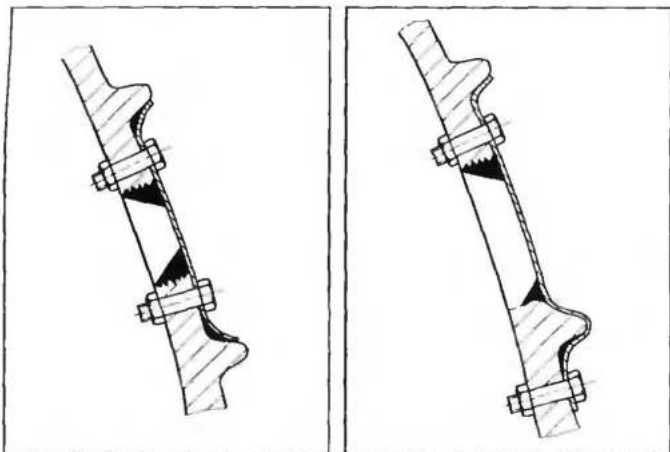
Схема установки одинарной стальной накладки на пробойну в стенке блока цилиндров внутри поверхности, ограниченной ребрами жесткости
